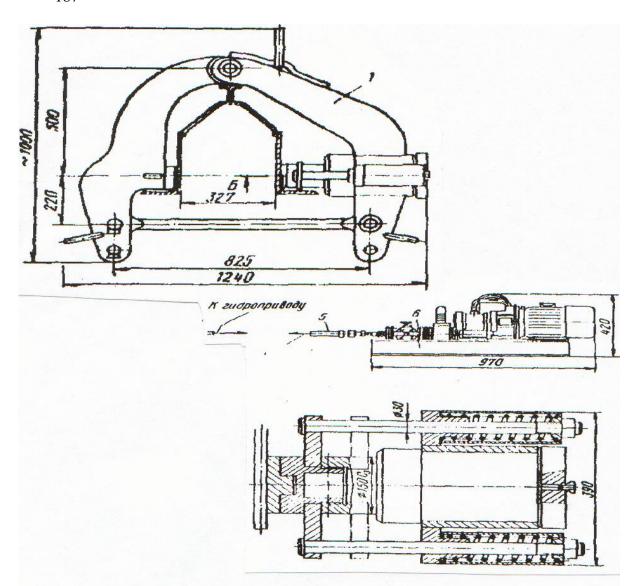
Пресс гидравлический для правки уширений хребтовых балок: 1 - скобы; 2 - муфта; 3 - штуцер; 4 - наконечник для заделки рукавов; 5 - рукав длинной 5000 мм; 6 - гидропривод.
